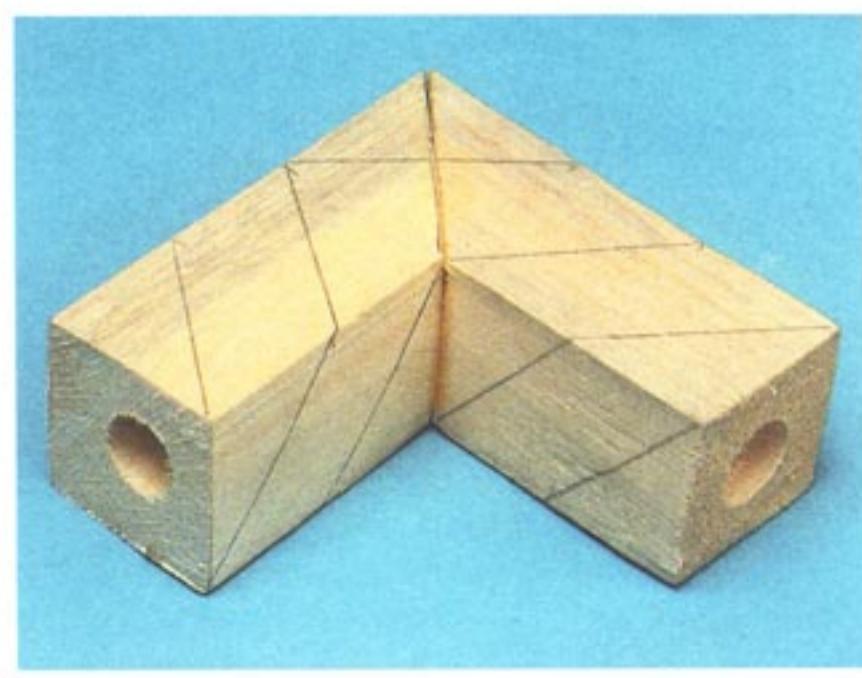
Разметка заготовки из двух деталей (вид спереди)
